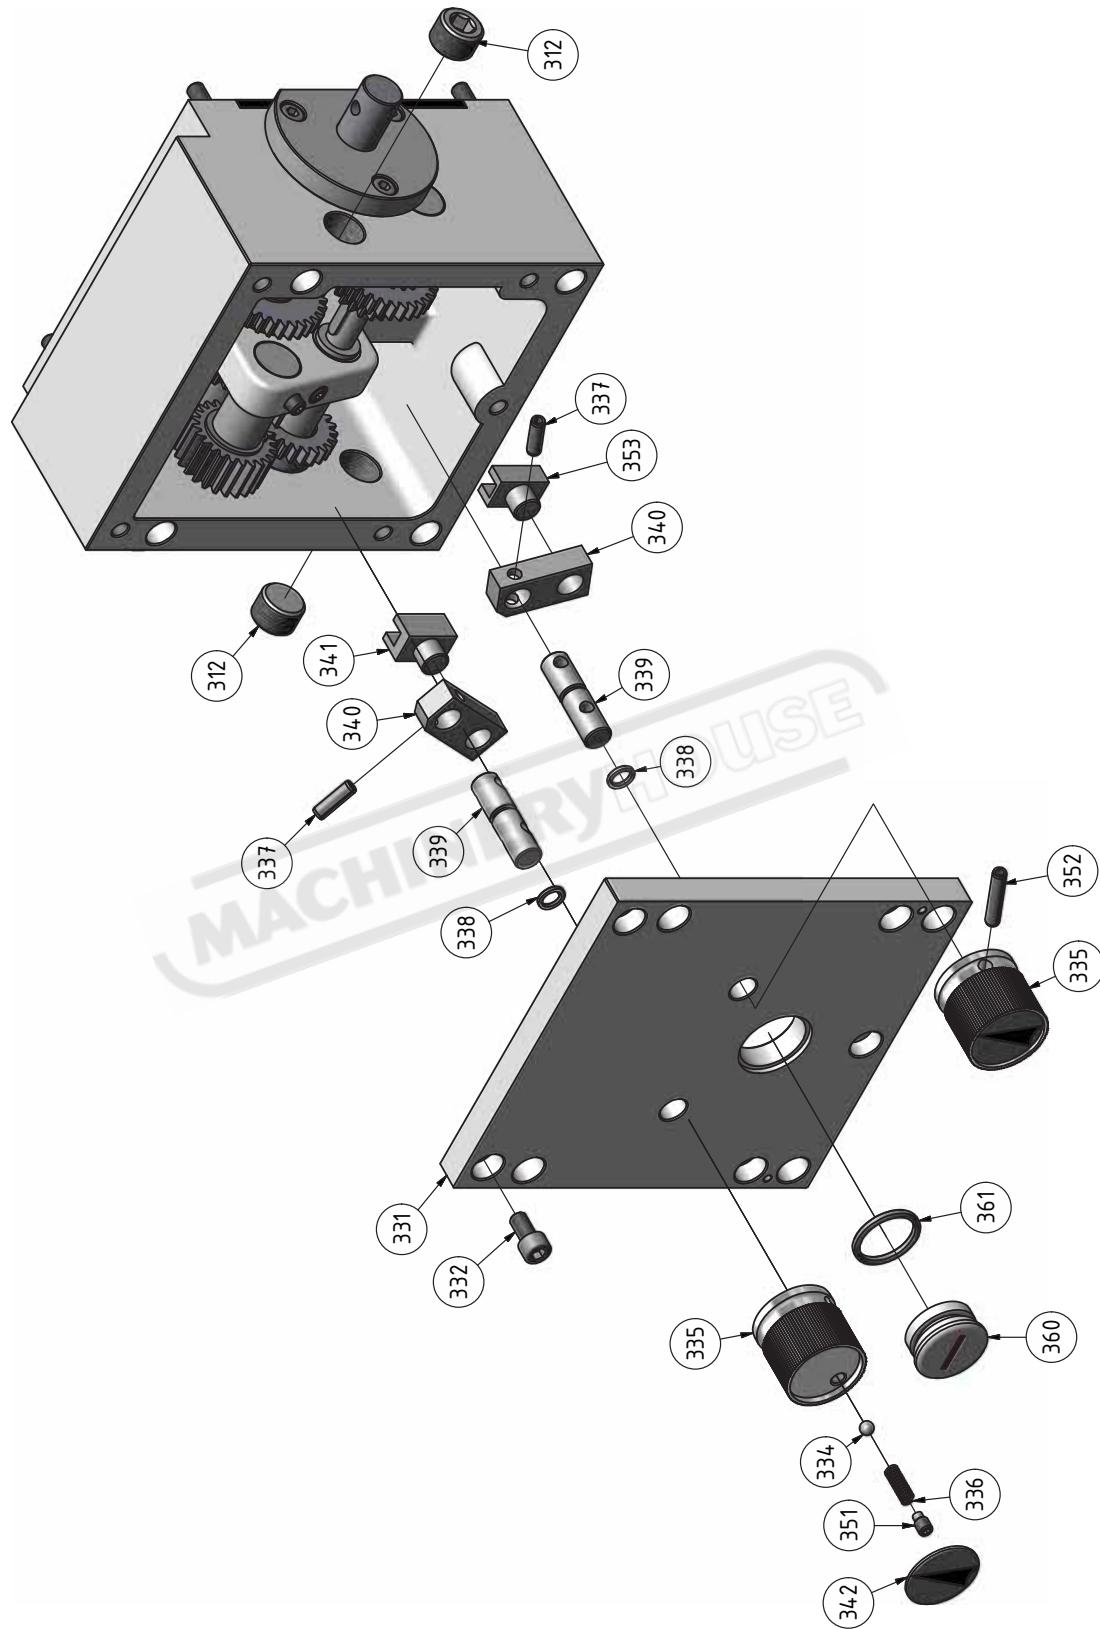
Vorschubgetriebe 1 von 2 - Feed gear 1 of 2 - TU 2506
